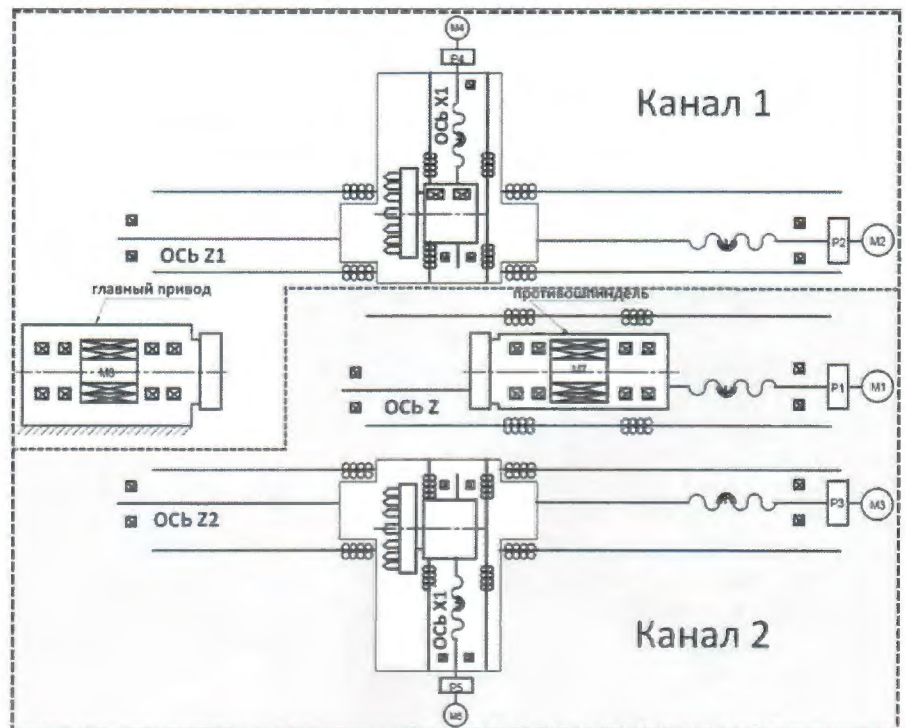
Кинематическая схема обрабатывающего центра наклонной компоновки
